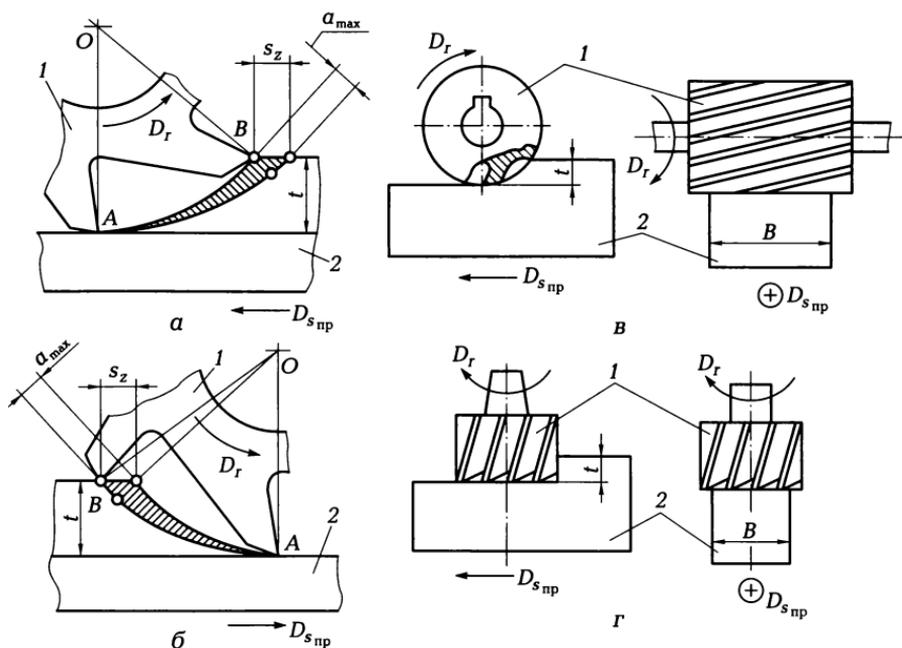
Схемы фрезерования против движения подачи (а) и по движению подачи (б) цилиндрической (в) и торцовой (г) фрезами:
